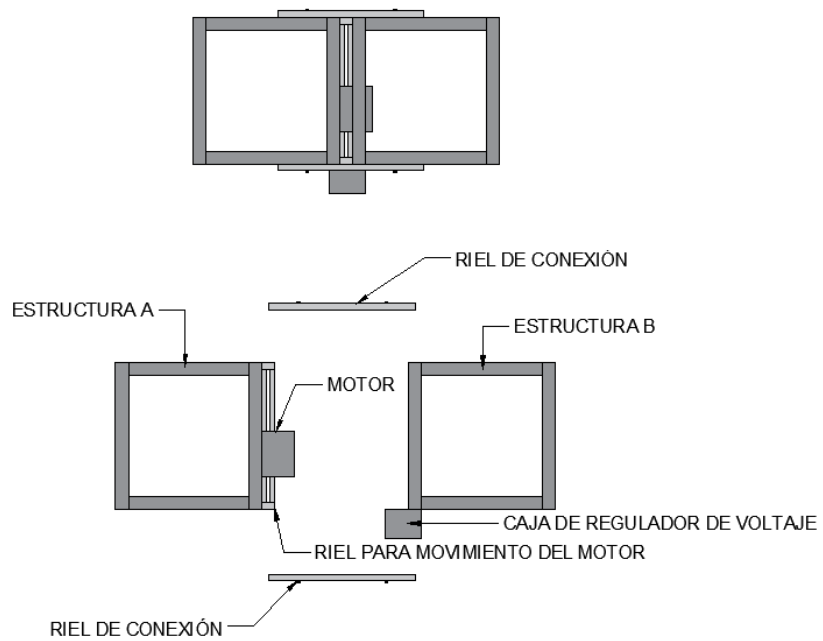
13 Vista en planta de la estructura metálica y sus partes.
